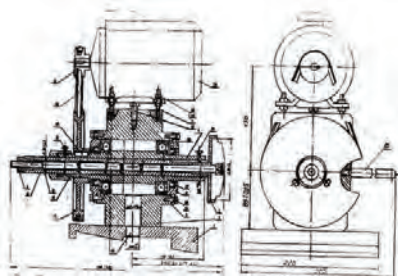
Приспособление для шлифовки сферы распределителей гидронасосов на станке
